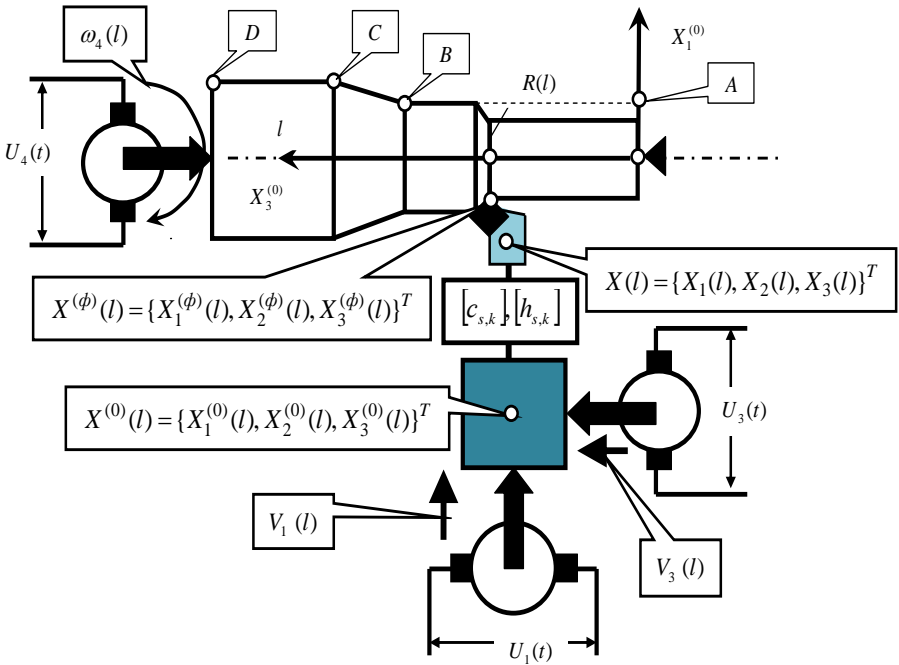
Схема управления формообразующими движениями инструмента относительно заготовки при точении
